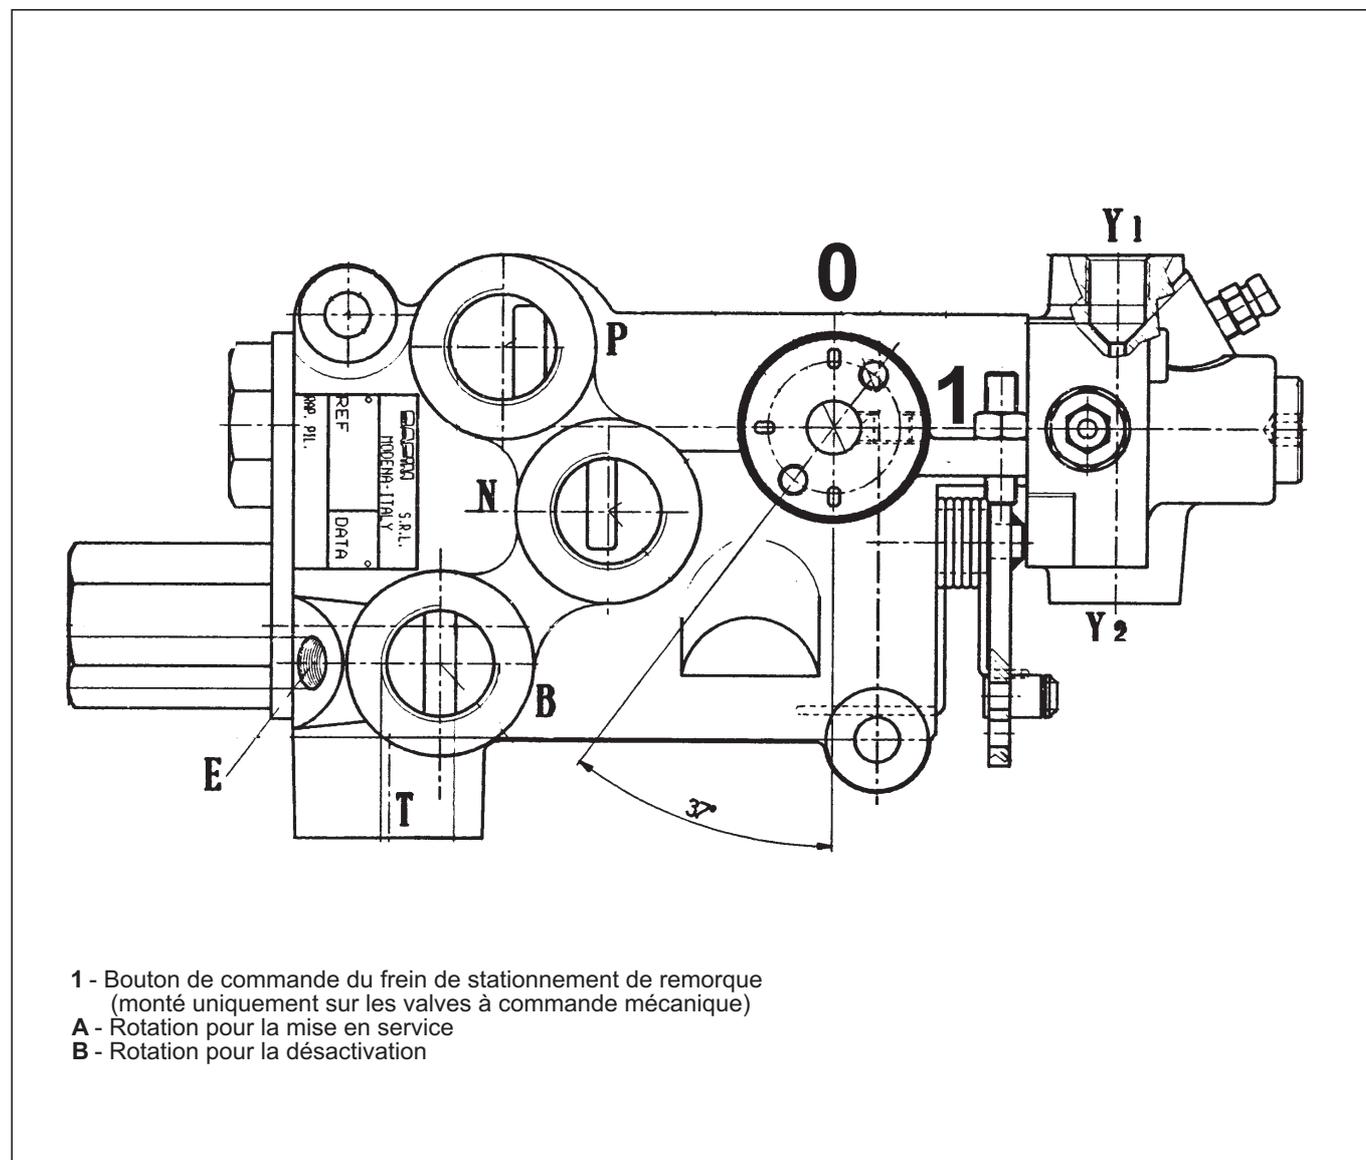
Distributeur pour le freinage hydraulique de remorque.
